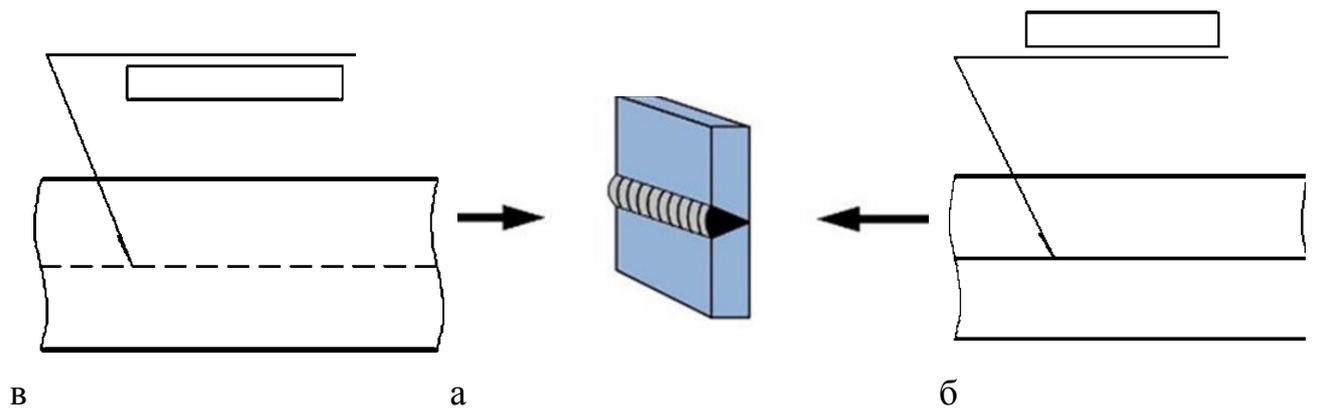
Образец схемы нанесения условного обозначения сварного шва
